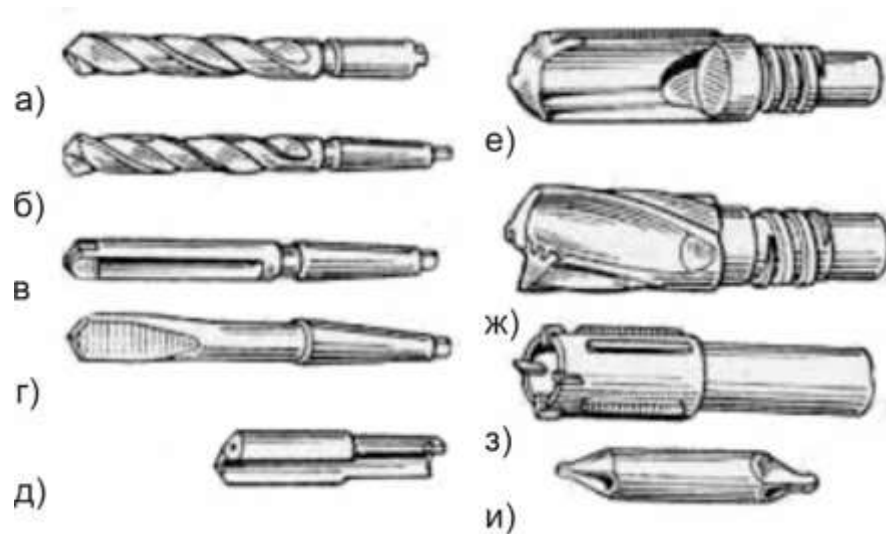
Основні типи свердл: а - спіральне з циліндричним хвостовиком; б - спіральне з конічним хвостовиком; в – рушничне свердло; г – свердло одностороннього різання; д – напівкругле свердло; е - гарматне свердло; ж – ежекторне свердло; з-трубчасте свердло; и - центрувальне свердло.
